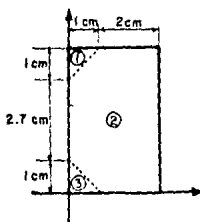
Dimensiones de la pieza # F del Yugo Escocés
